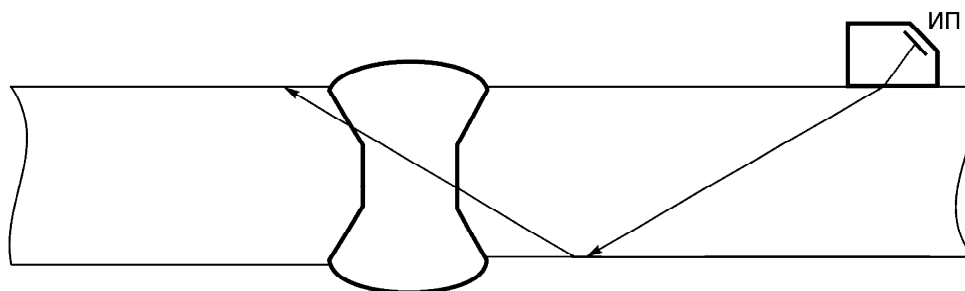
Схема прозвучивания стыкового сварного соединения однократно-отраженным лучом
